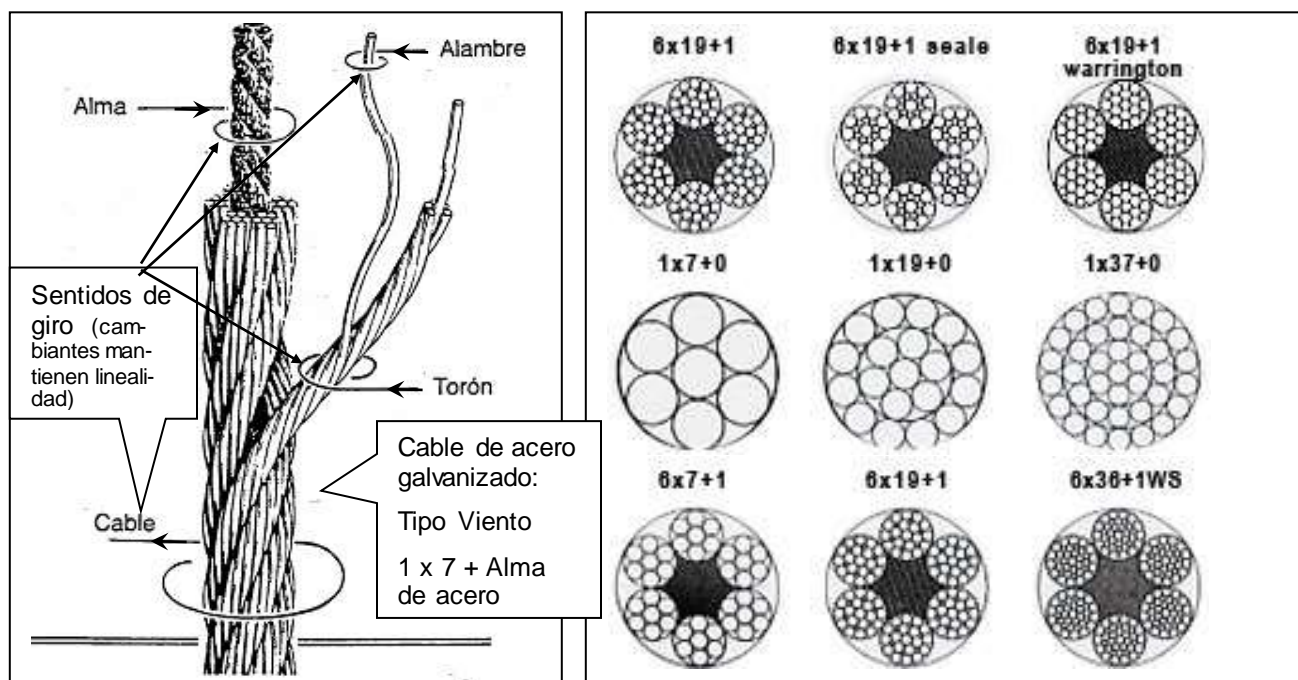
Cables de Acero: Conformación - Tipos
